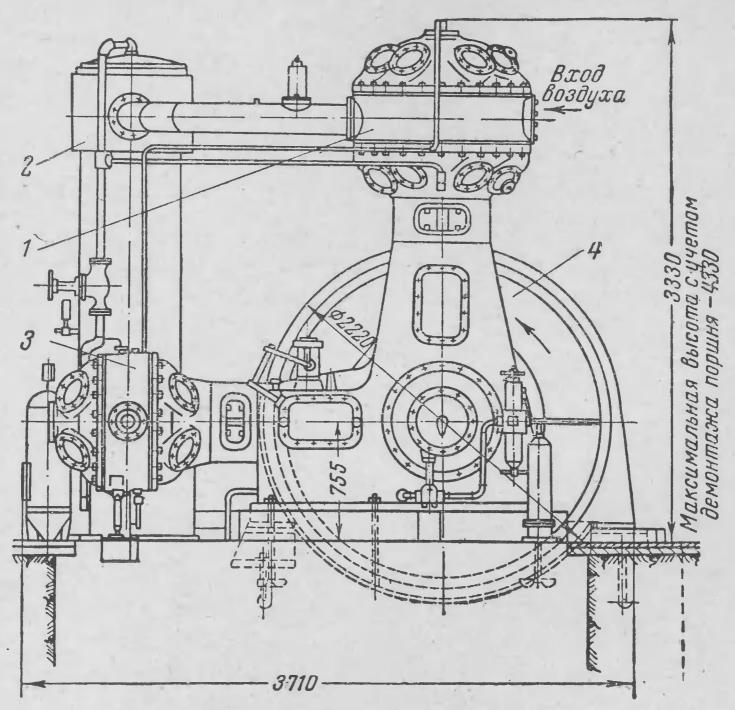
Компрессор ВП-50/8 (воздушный, двухступенчатый, угловой, двойного действия).
